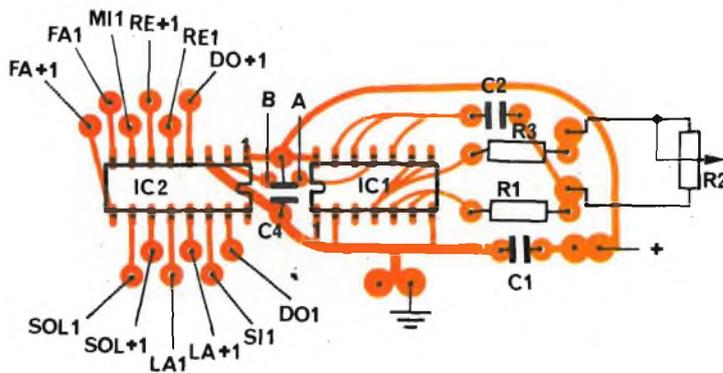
/A - Circuito stampato visto dal lato componenti del generatore d'ottava superiore.
